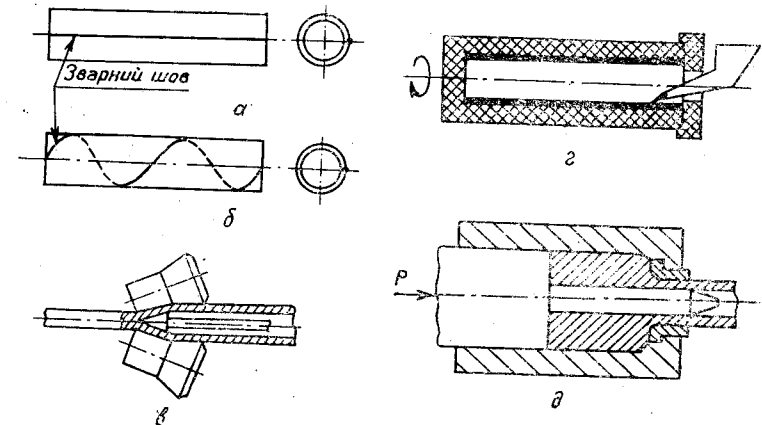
Способи виготовлення трубчастих заготовок:
